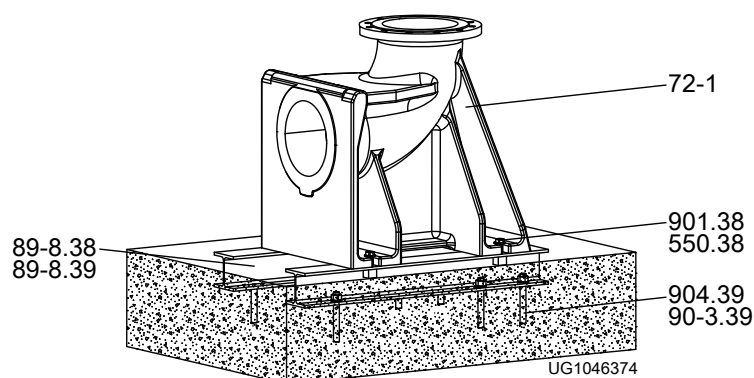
Крепление опорного фланцевого колена с помощью фундаментных направляющих и соединительных анкеров
